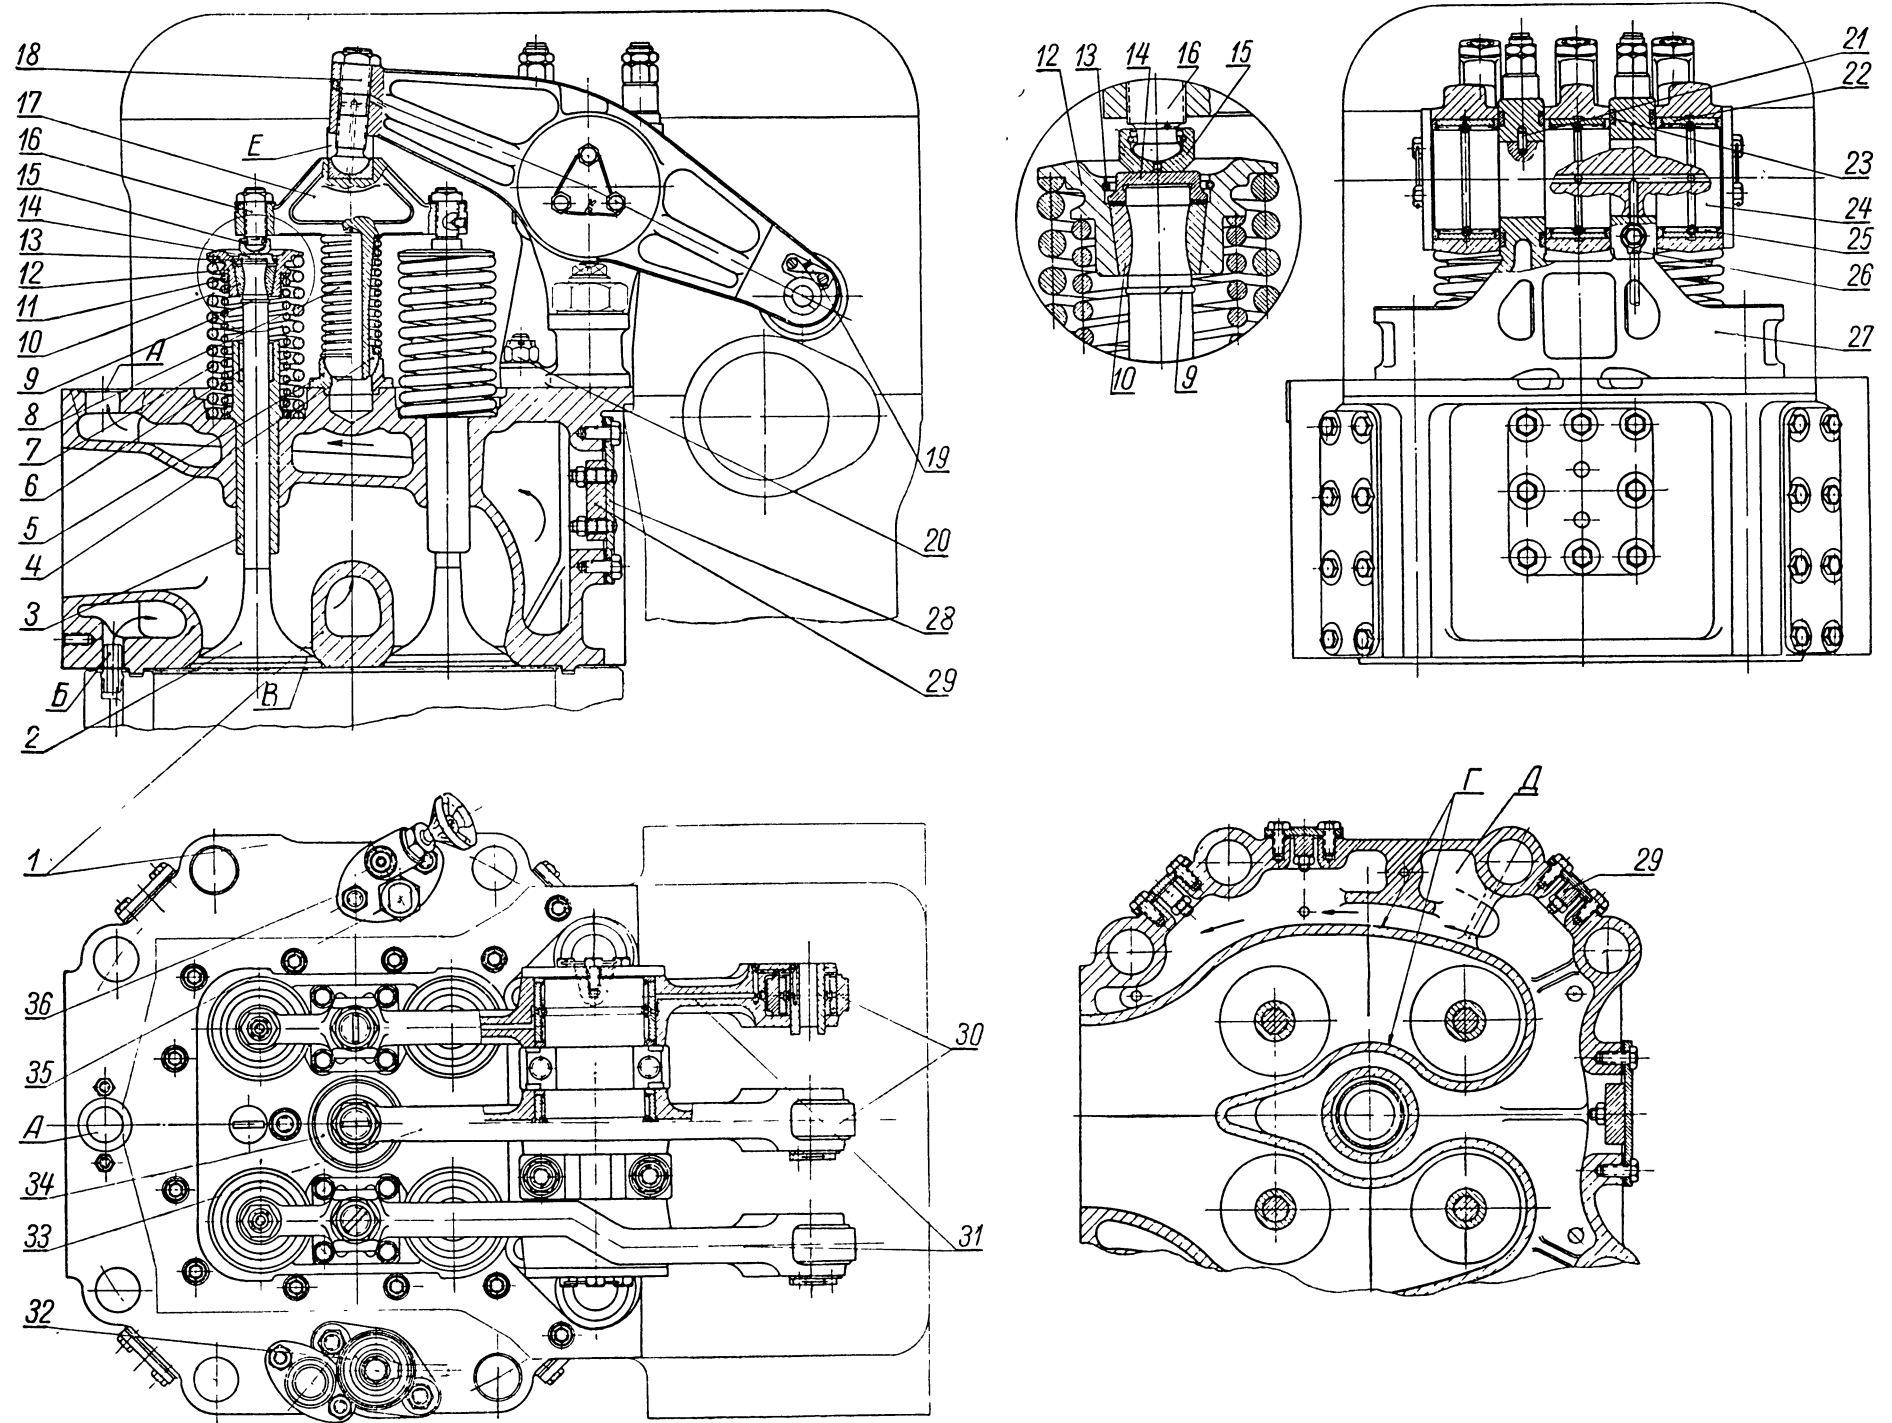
Крышка цилиндра с рычагами и клапанами.
